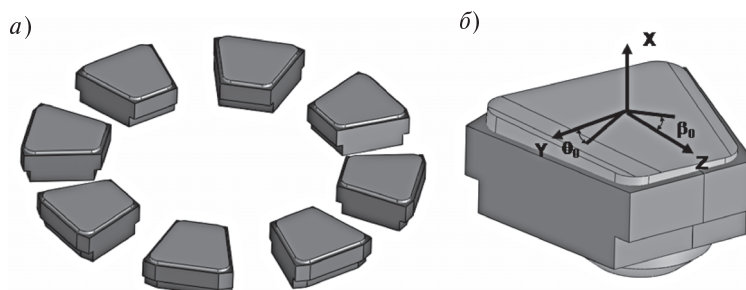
Схема расположения сегментов (а) и 3-D CAD-модель (б) сборки сегмента и его накладки
